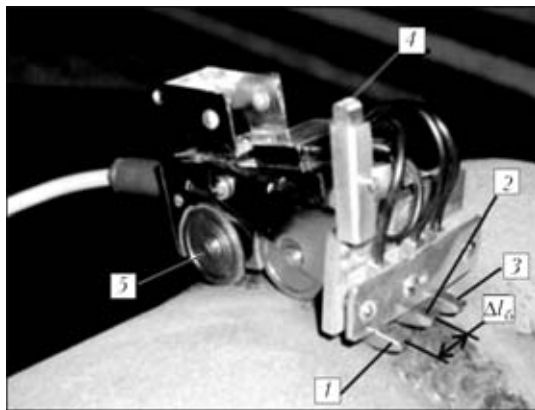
Устройство для контроля стыковых сварных соединений труб многоканальным сканирующим устройством прибора типа ИКН: 1–3 — феррозондовые преобразователи сканирующего устройства для регистрации поля  $H_p$  на поверхности сварного шва; 4 — феррозондовый преобразователь для отстройки от внешнего магнитного поля  $H_p$ ; 5 — колеса привода измерителя длины;  $\Delta L$  — базовое расстояние между феррозондовыми преобразователями
